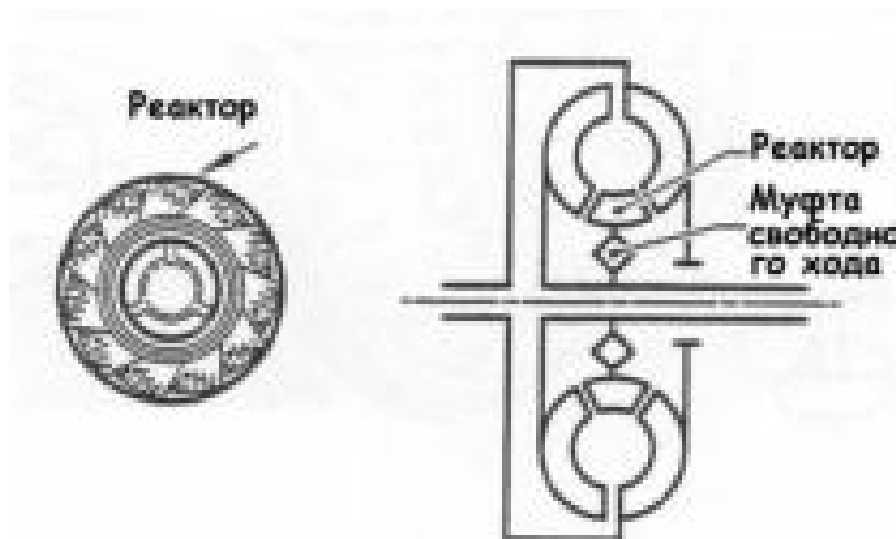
Реакторное колесо конвертора (гидротрансформатора).
